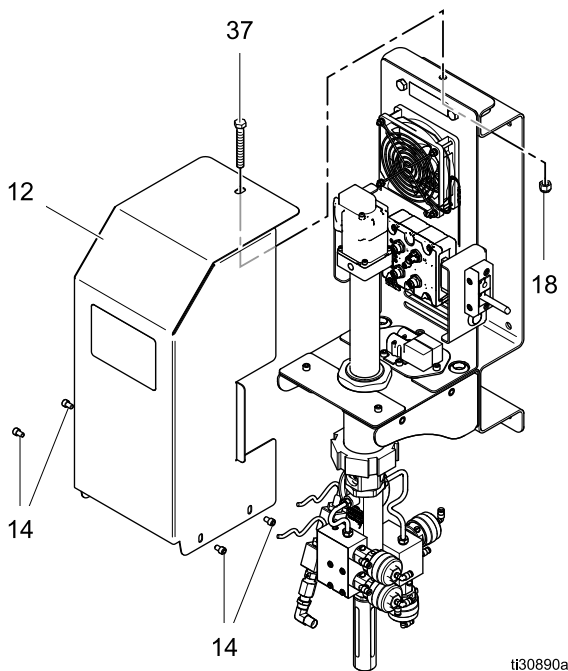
Abdeckung von Nachrüstanzug installieren (Wandmontage)
